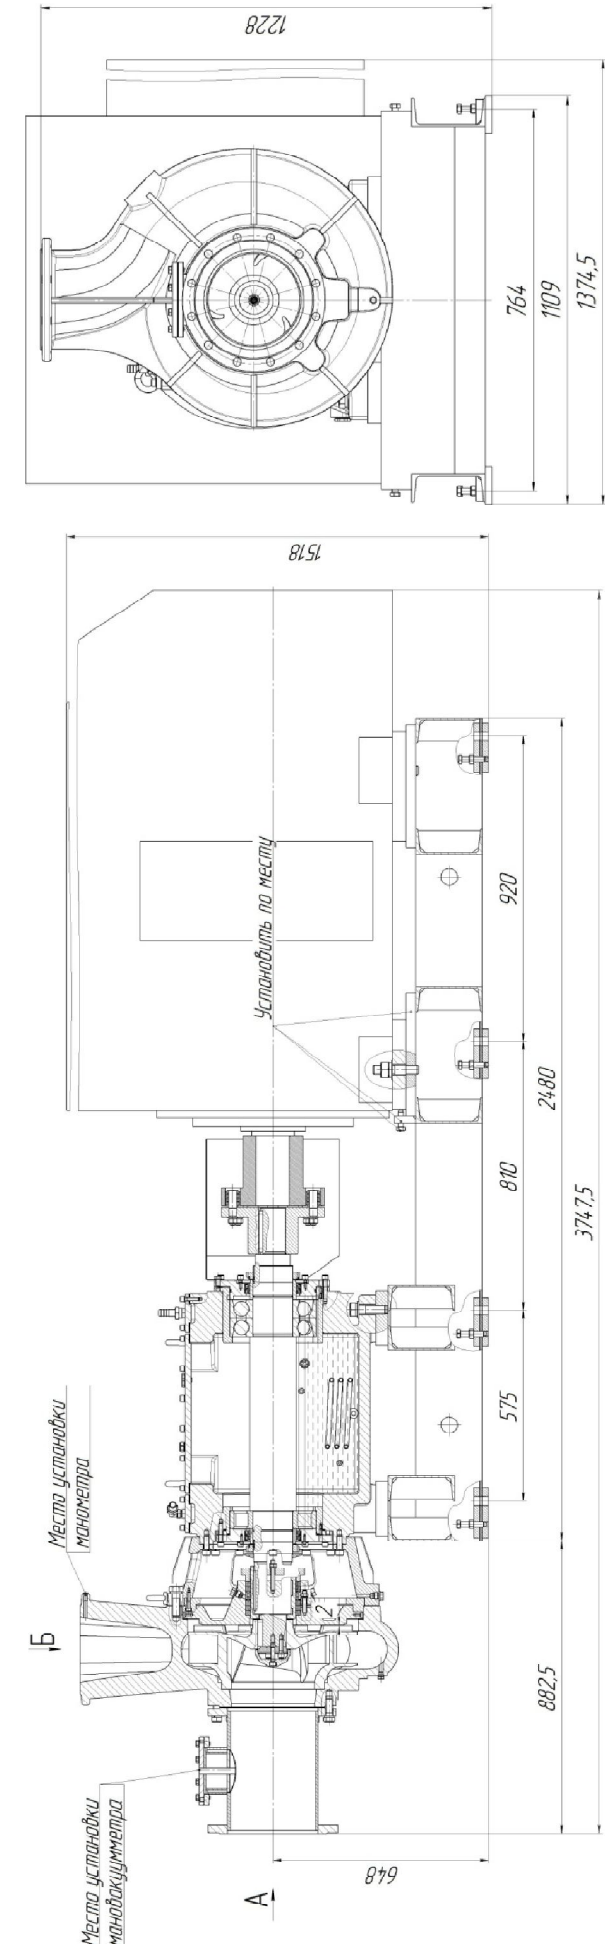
Габаритные и присоединительные размеры электронасосного агрегата
